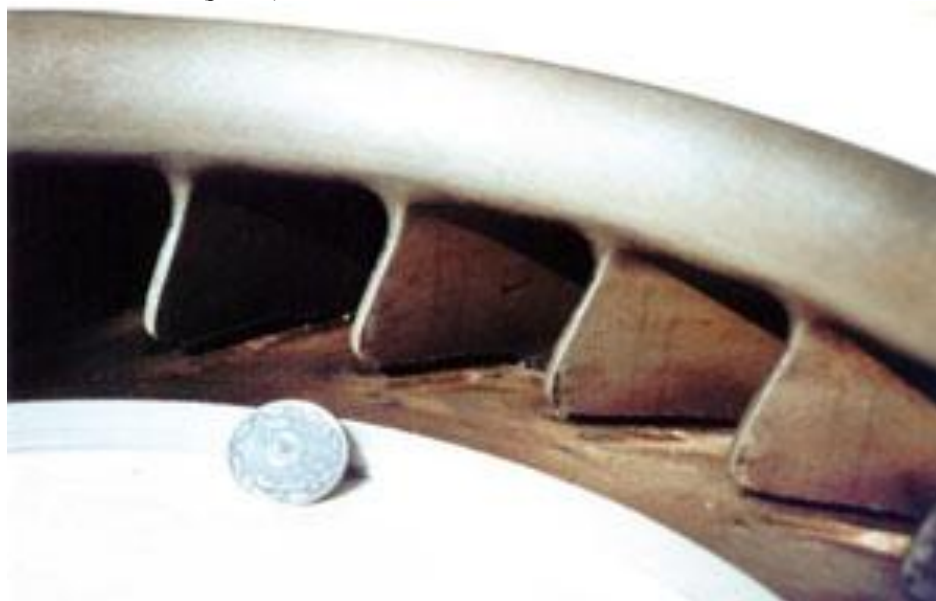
Эрозионный износ лопаток колеса 1-й ступени ротора воздушного компрессора КВД модели 2MCL - 456 фирмы "Хитачи" (Япония)
